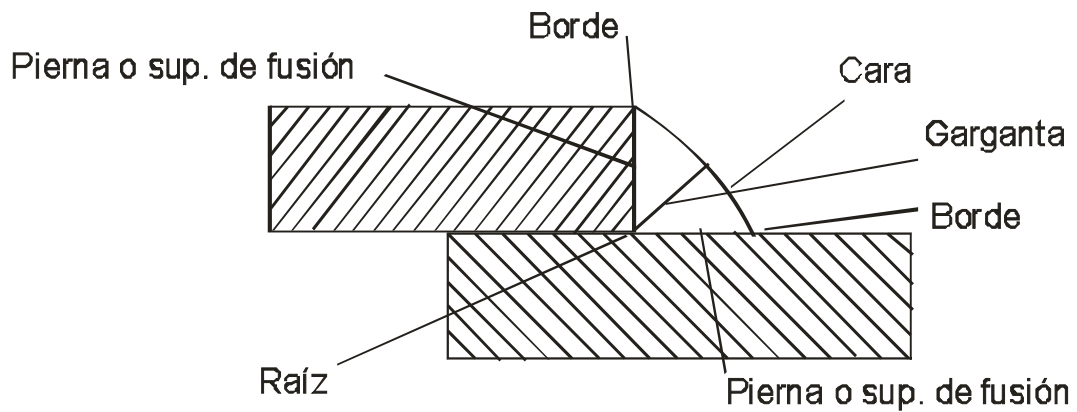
Diagrama de las partes de la soldadura.
